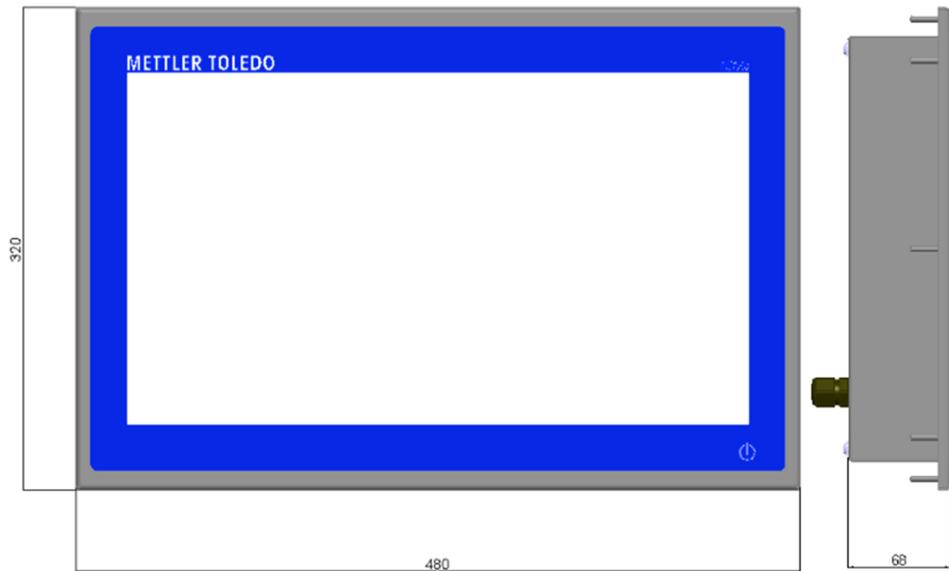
Dimensiones de IND970-19-HMI para el montaje en cuadro de control
